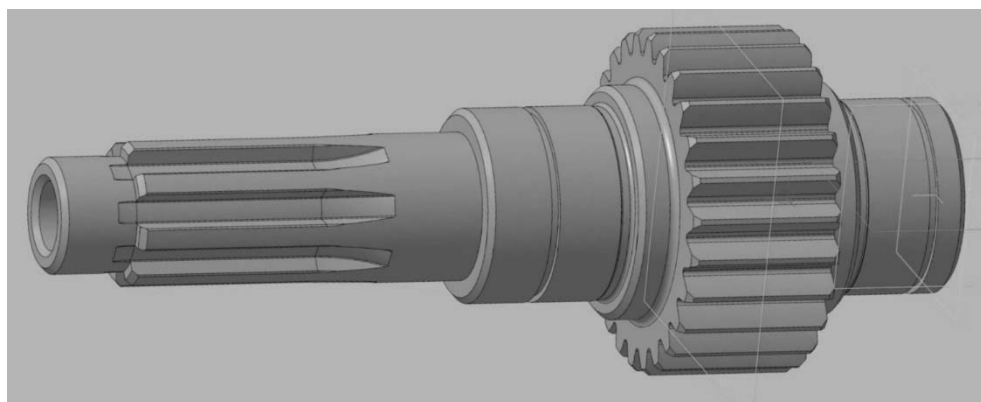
Пример объемной модели детали со стандартными элементами на ее поверхности
